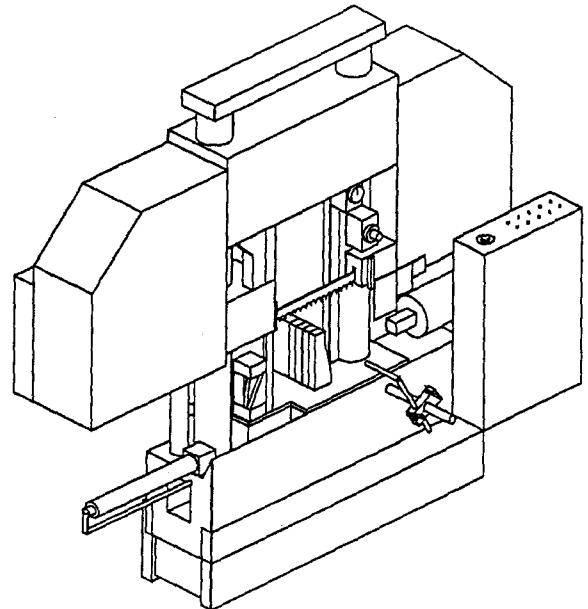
Горизонтальний стрічковопиляльний верстат з колоною
